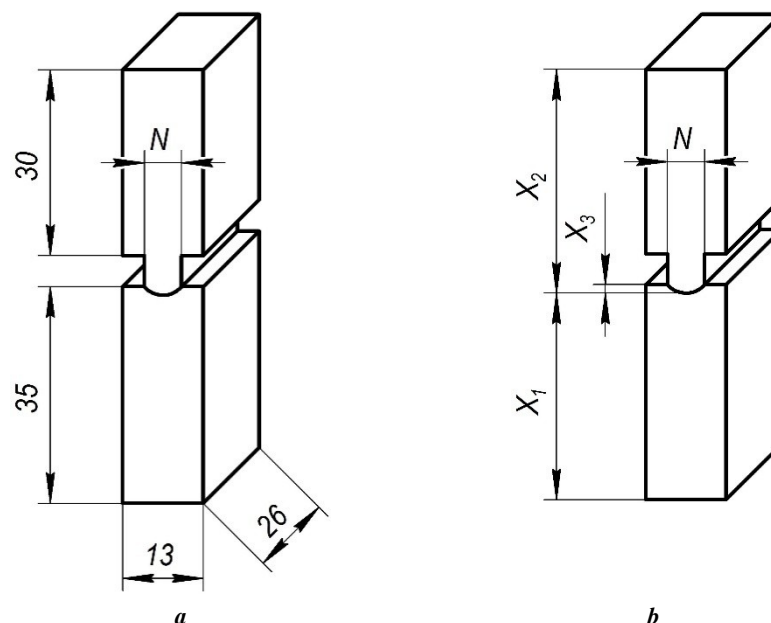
Образец: а – полученный ЛСТ; б – схема обмера осадки компонентов
